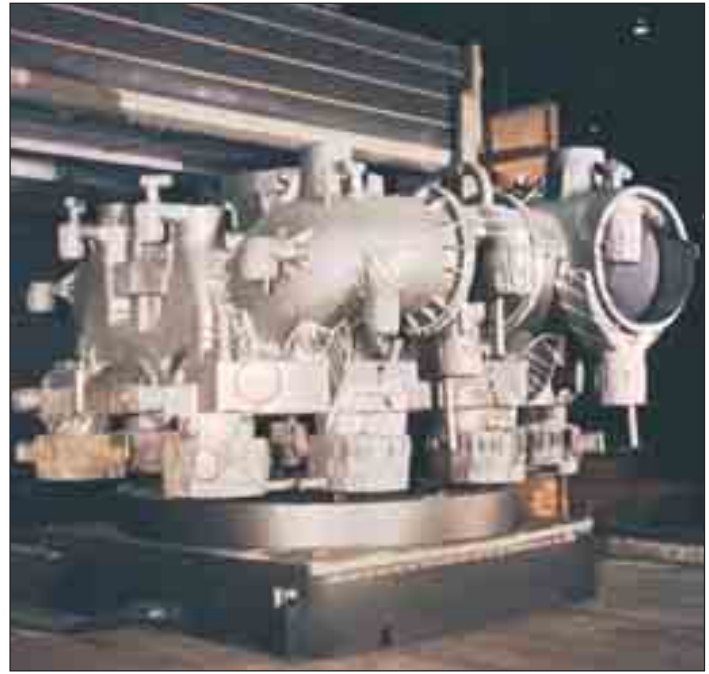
In der Form im Bild 2 gegossenes Turbinengehäuse-Unterteil mit vollständiger Gießtechnik
